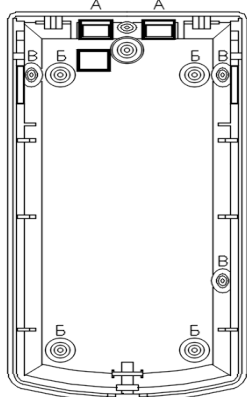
Внешний вид внутренней стороны основания корпуса извещателя
